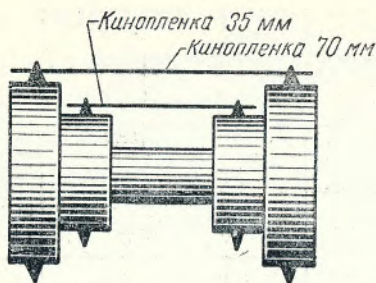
Комбинированный зубчатый барабан кинопроектора для транспортировки 70- и 35-мм фильмов
